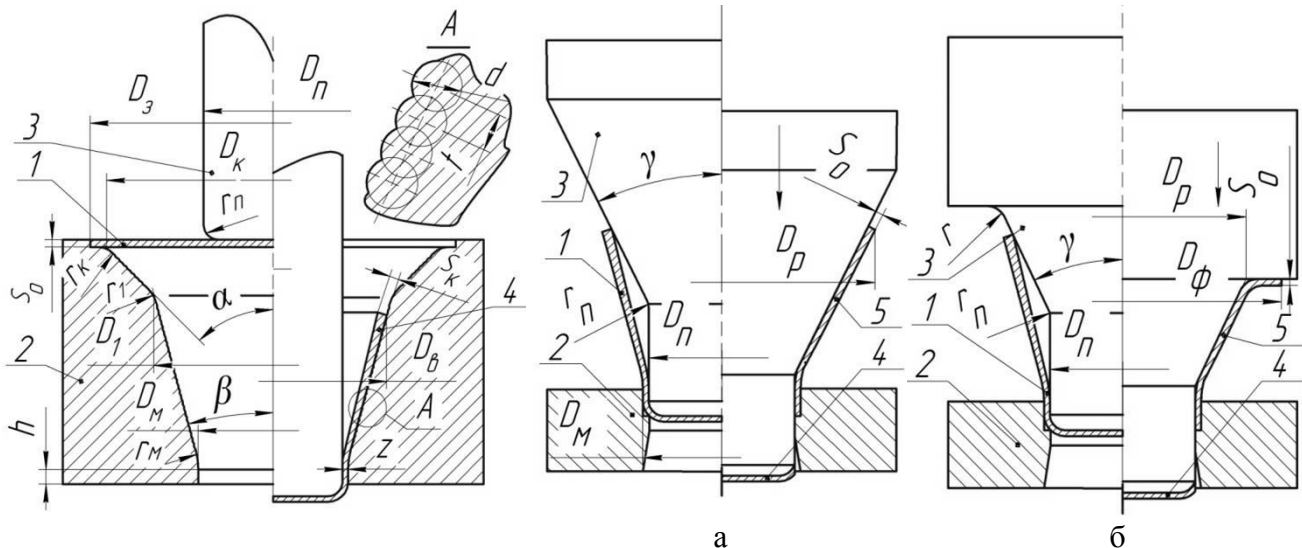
Вытяжка листовой заготовки в двухконусной матрице специального профиля для получения полуфабриката
